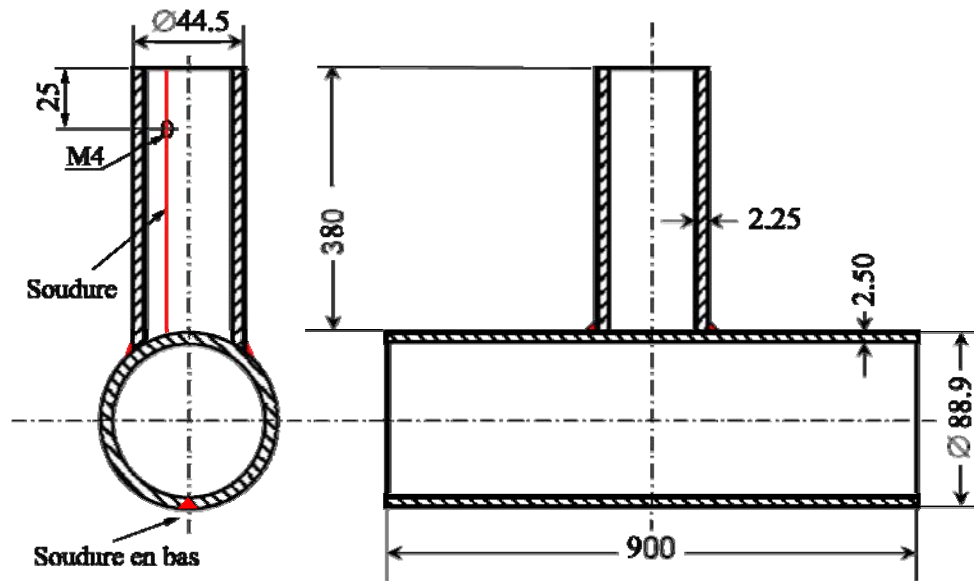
Dimension de la jonction soudée T utilisée dans les essais de flexion rotative (mm)
